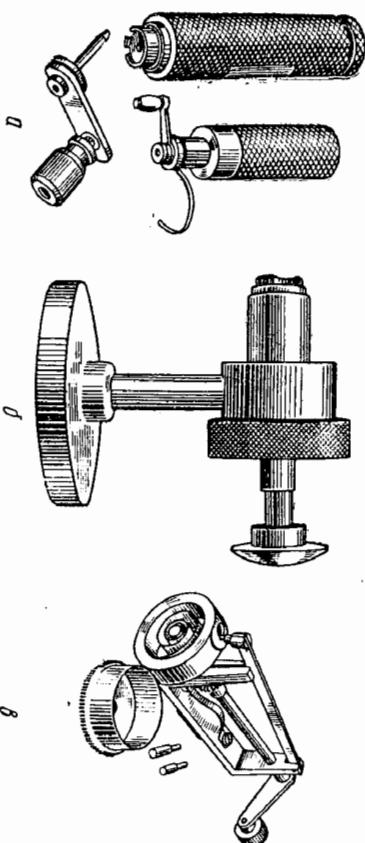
Приспособления для навивки и вставки пружины в барабан:
